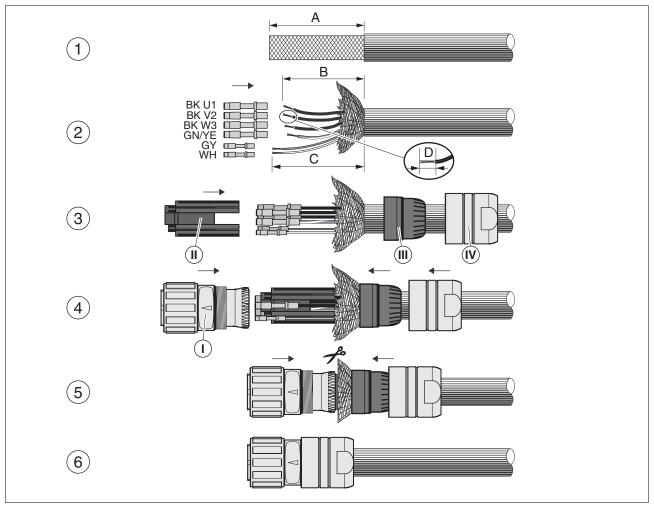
Assemblare il cavo motore con connettore motore M40
